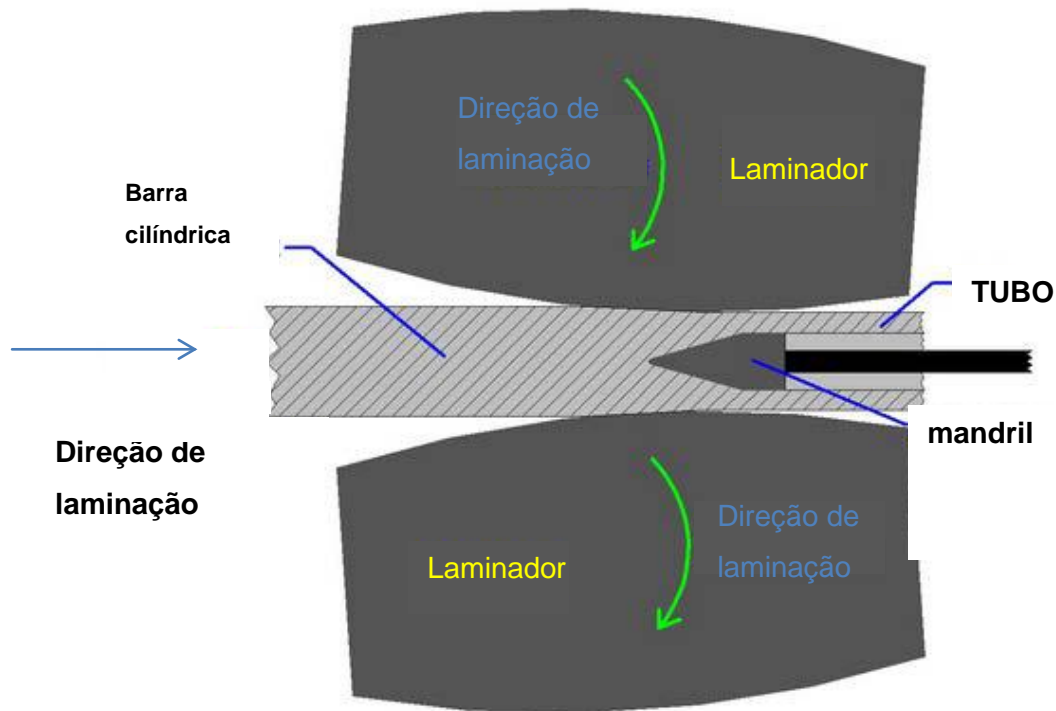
Esquema do laminador perfurador, mostrando o posicionamento oblíquo dos rolos laminadores e a passagem do mandril, ao abrir um diâmetro interno [16].
